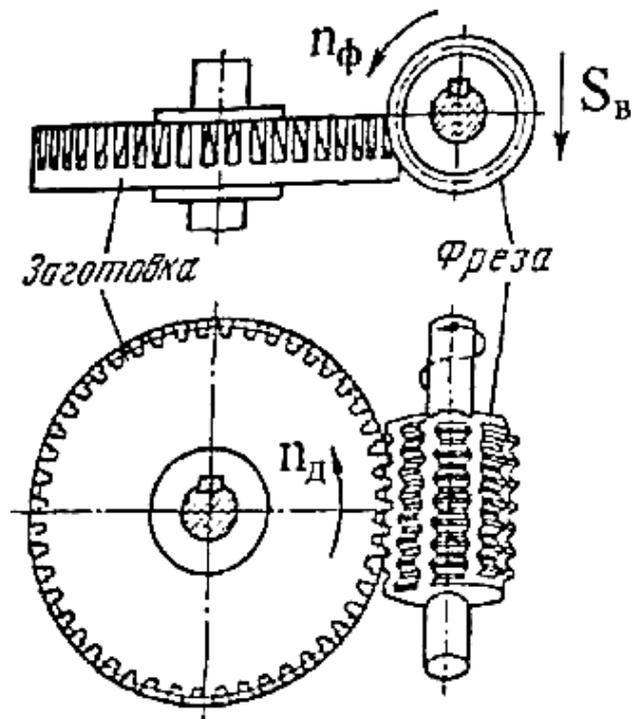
Схема нарезания зубьев червячной фрезой
